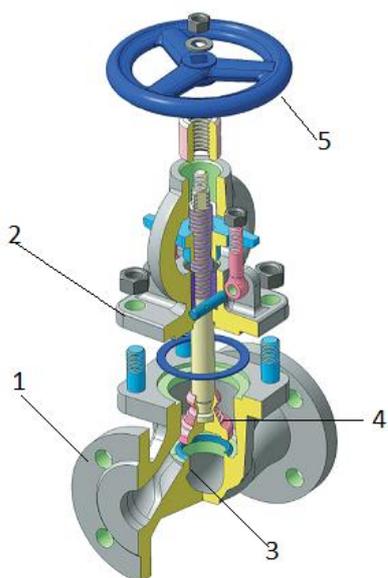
Запорный клапан с ручным управлением: 1 – корпус; 2 – крышка; 3 – седло; 5 - маховик
